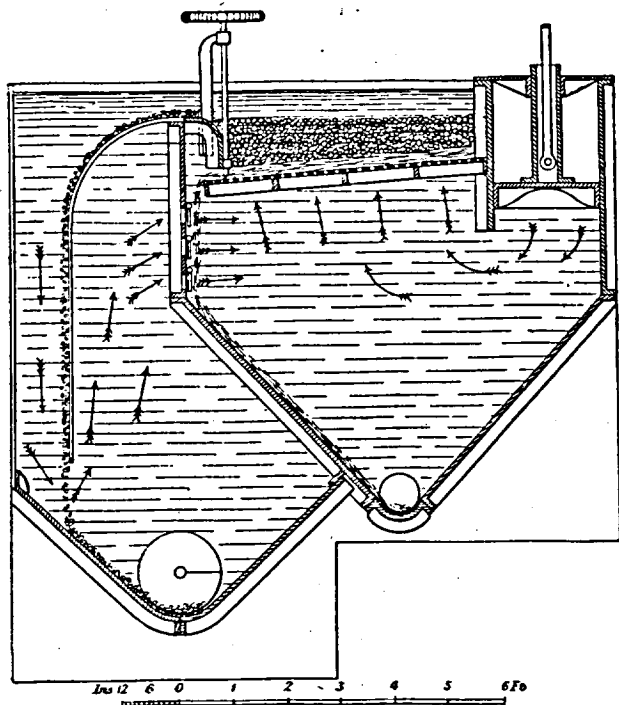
Coupe verticale: jig à gailletes Sheppard.
